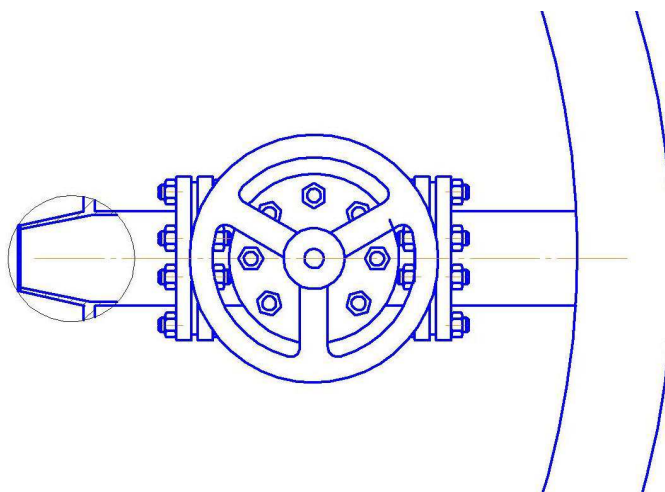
Напорный патрубок напорно-размывной линии (вид сверху)
